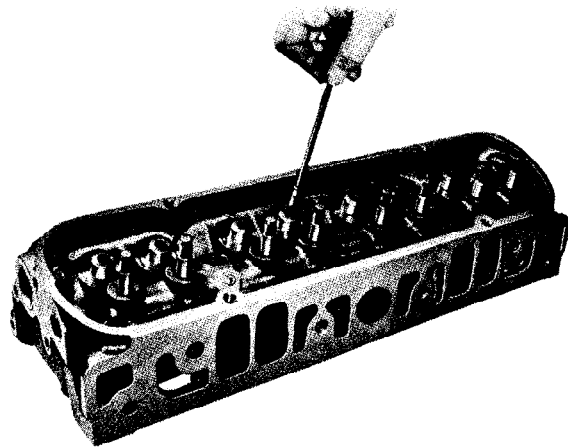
Limpieza de una guía de válvula por medio de un limpiador de láminas ajustables (Pontiac Motor Division of General Motors Corporation).
